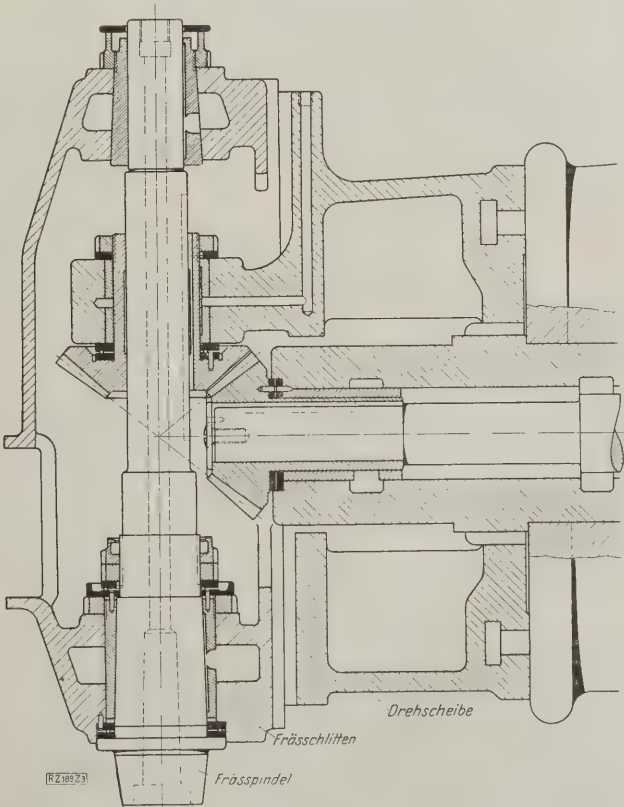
Spindelantrieb und -lagerung der Rundtisch-Fräsmaschine
